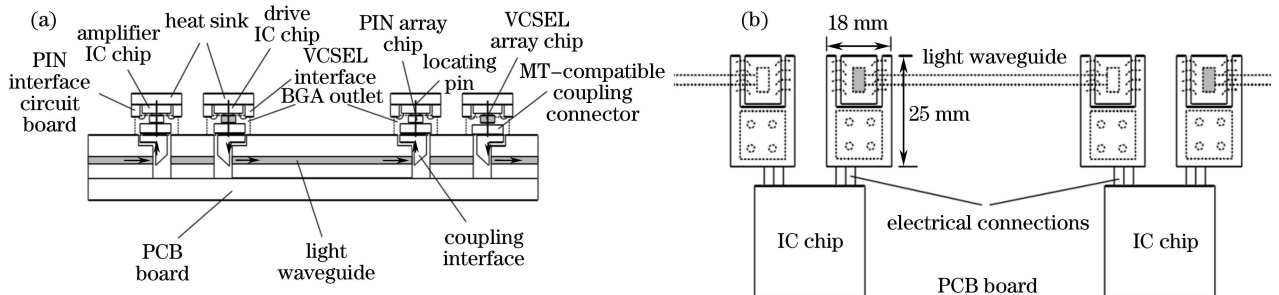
(a) 华中科技大学光电互联 PCB 原理图; (b) EOPCB 俯视图
